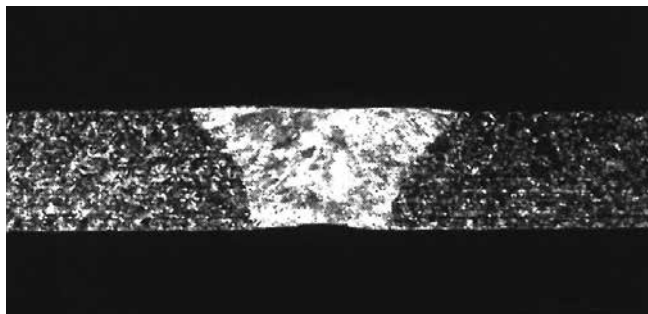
WIG 轨道焊缝的横截面图像
